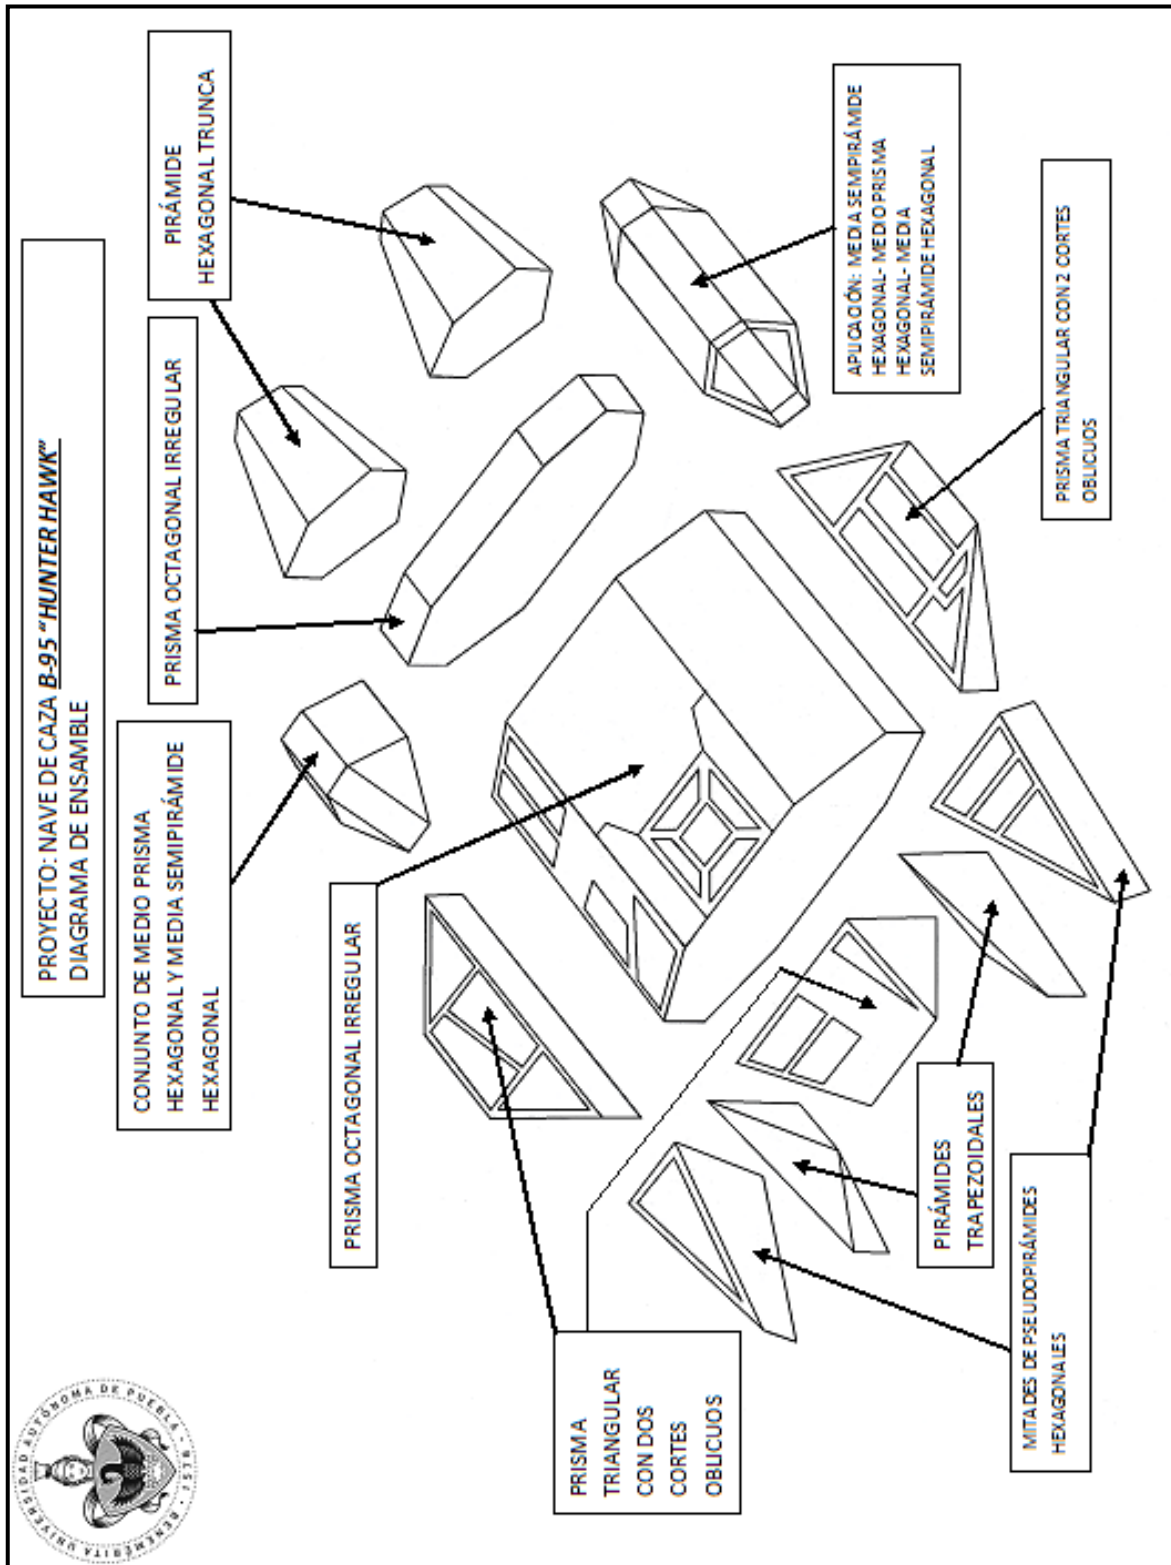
Práctica 40, Hunter Hawk, vista explosionada
